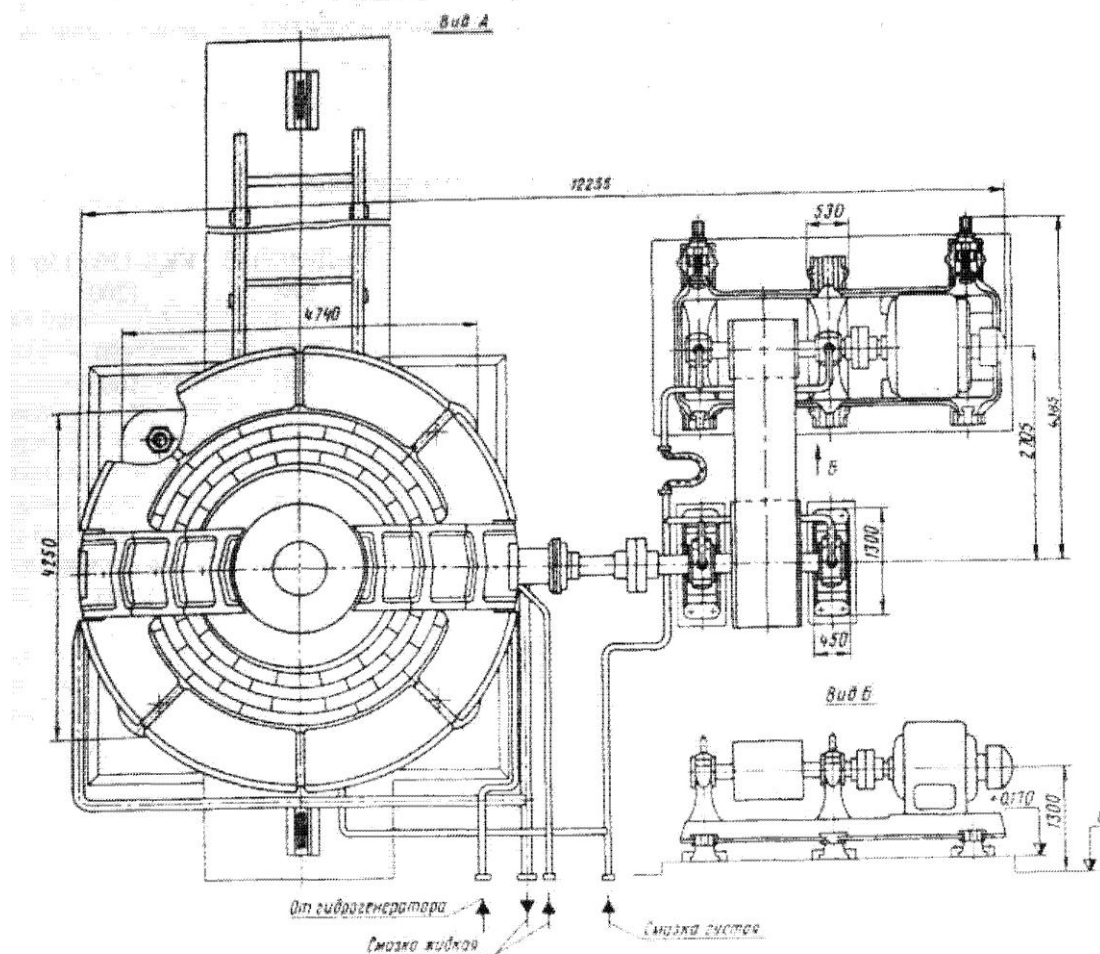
Конусна дробарка ККД-1500/300 (вид зверху)
